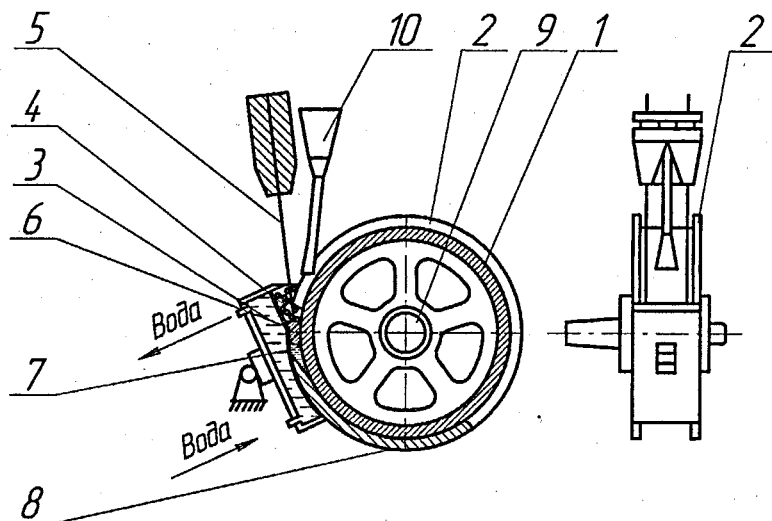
Електрошлакове наплавлення: 1 – наплавлювана деталь; 2 – габаритні диски; 3 – кристалізатор; 4 – флюс; 5 – електрод; 6 – шлакова ванна; 7 – ванна розплавленого металу; 8 – наплавлений шар; 9 – оправка; 10 – дозатор
